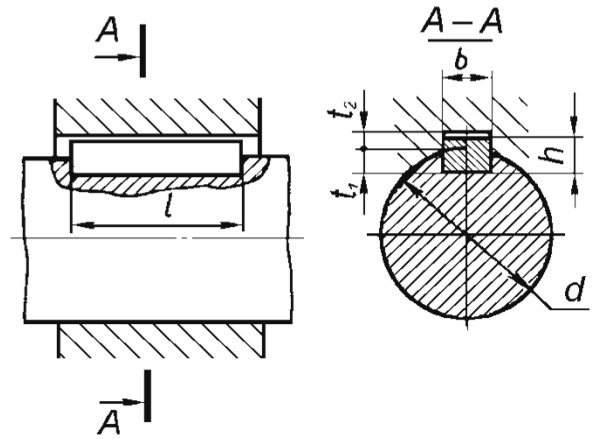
Конструкция соединения вала и ступицы детали с помощью призматической шпонки
